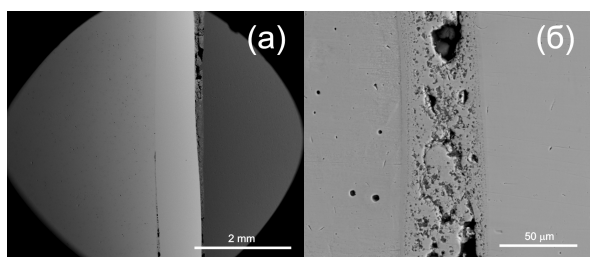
СЭМ изображения наблюдаемой морфологии области сварного шва для режима 6: общий вид (а); дефектная структура шва (б)
